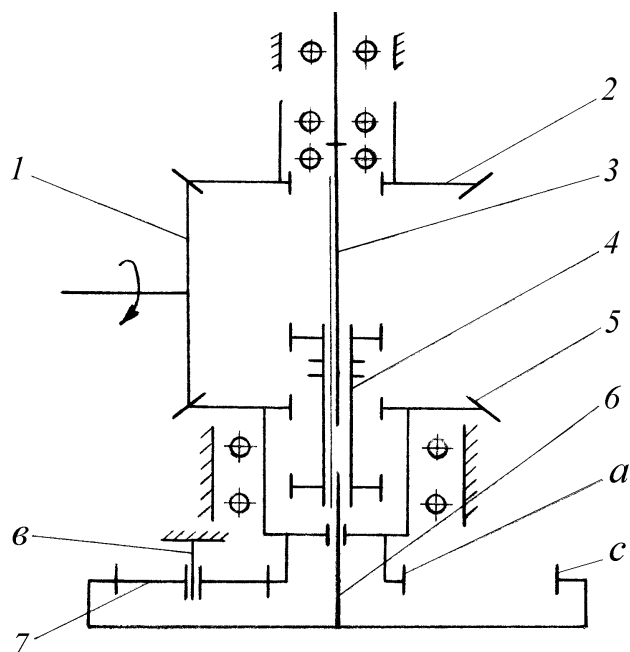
Схема планетарного ходоуменьшителя, встроенного в КП с поперечными валами
